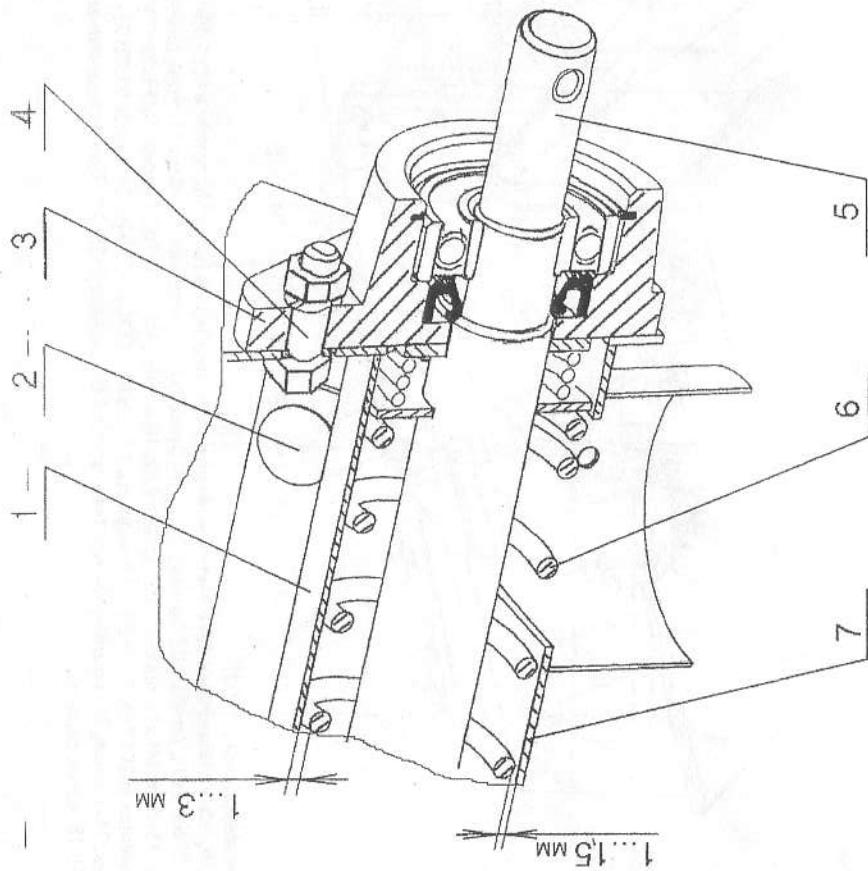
Схема регулировки аппарата туковысевающего АТП-2Г.
